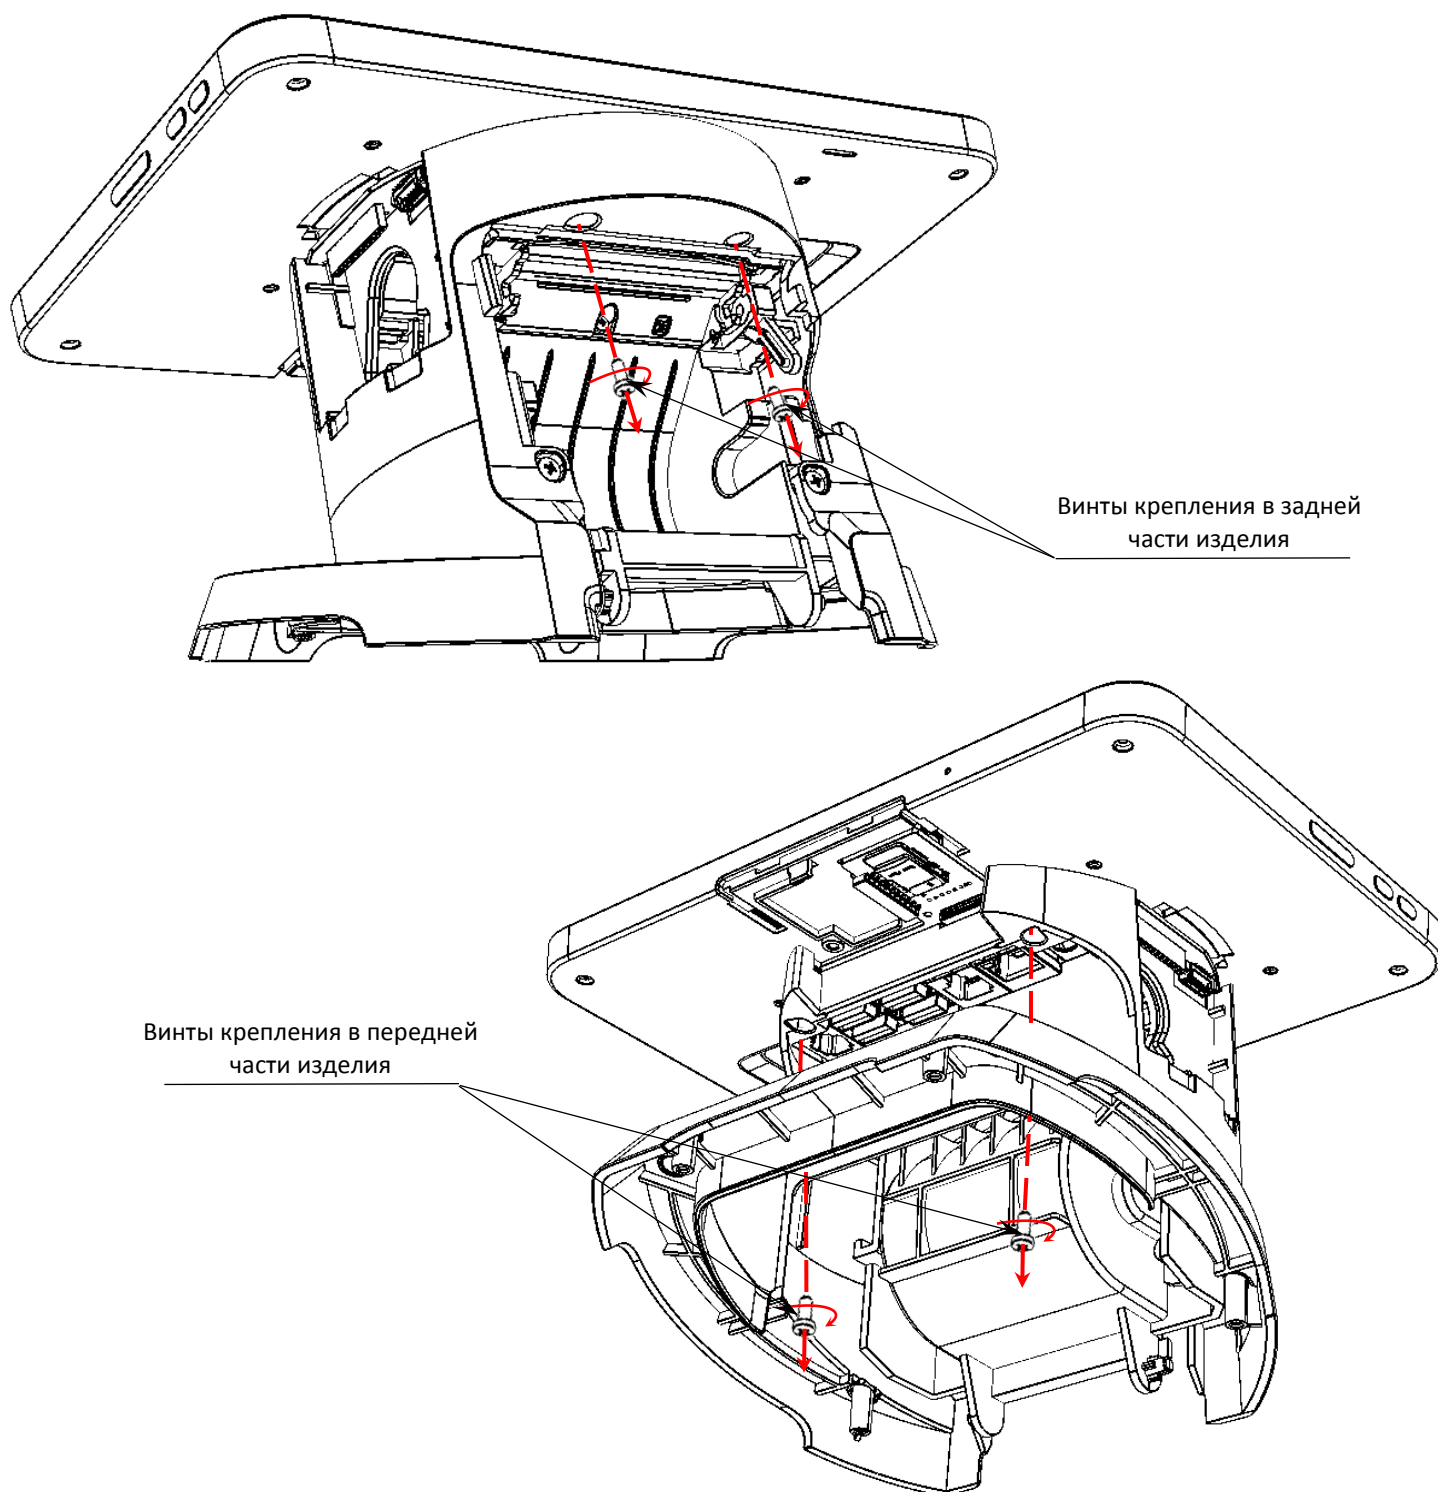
Винты крепления стойки к планшету в передней и задней части корпуса
